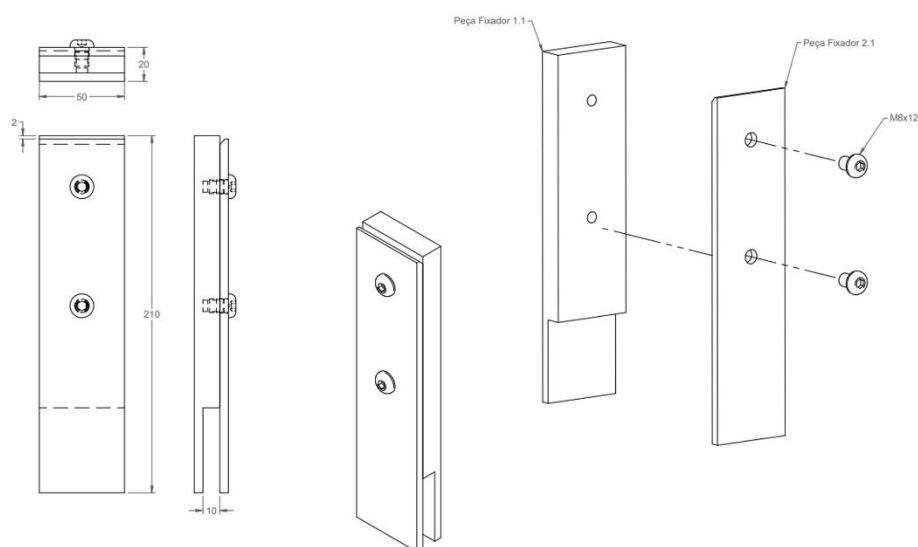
Pinça de fixação para a parte inferior da estrutura (vidros)
